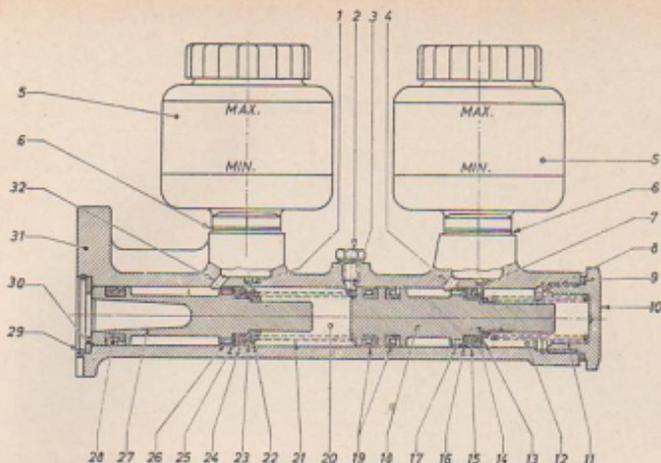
Tandem-Hauptbremszylinder mit aufgeschraubten Bremsflüssigkeitsbehältern im Schnitt
